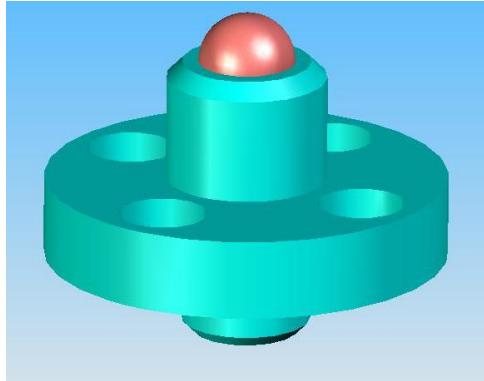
Apoio do ponto de ligação ao amortecedor
